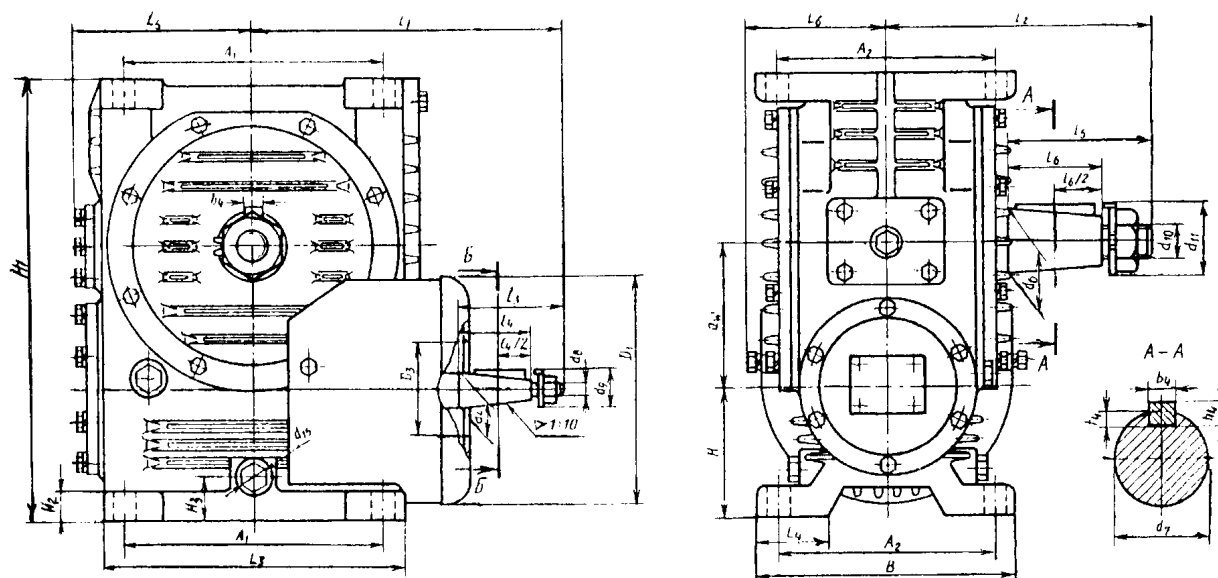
Редуктор червячный одноступенчатый типа Ч (a_w 50, 60, 80, 100, 125, 160) ГОСТ27701-88. Вал тихоходный в сборе с колесом и подшипниками вставляется в корпус через отверстие крышки, базируется на закрепленной крышке глухой, после чего устанавливается крышка подшипника сквозная с манжетой.
